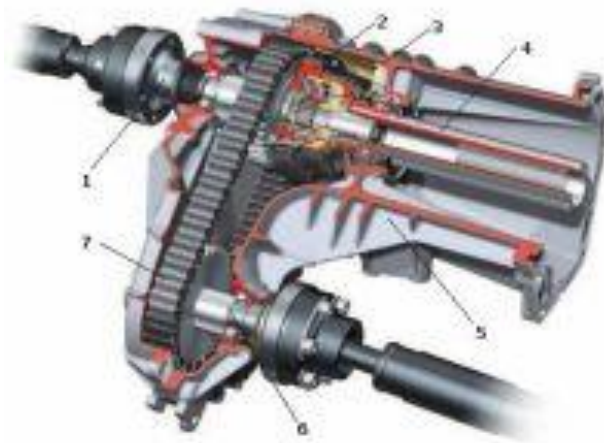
Загальний пристрій роздавальною коробки
